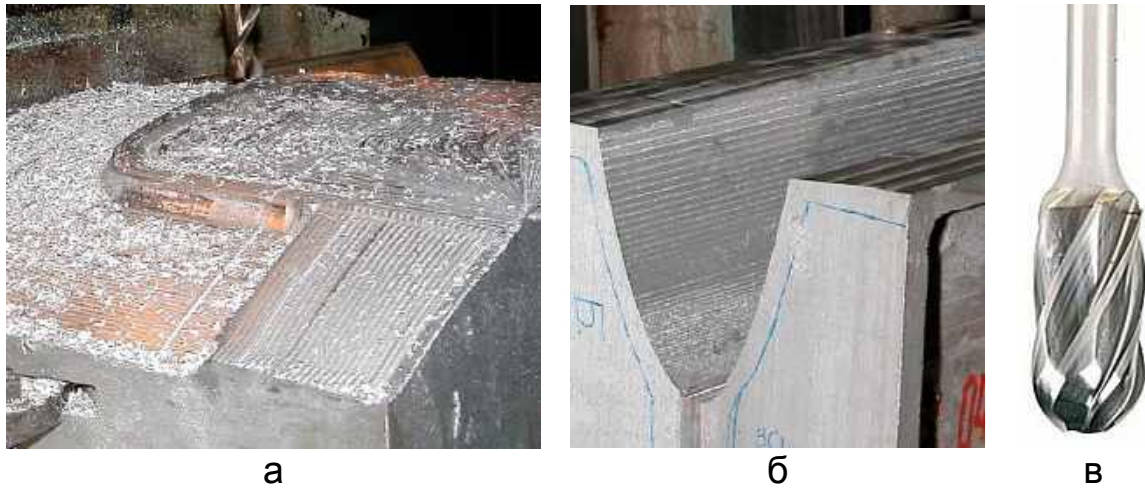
Загальний вигляд опуклої (а) та увігнутої (б) поверхонь заготовки після трикоординатного фрезерування кінцевою фрезою зі сферичним торцем (в)
